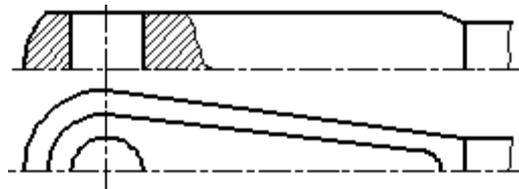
Образец оформления линий пересечения поверхностей
